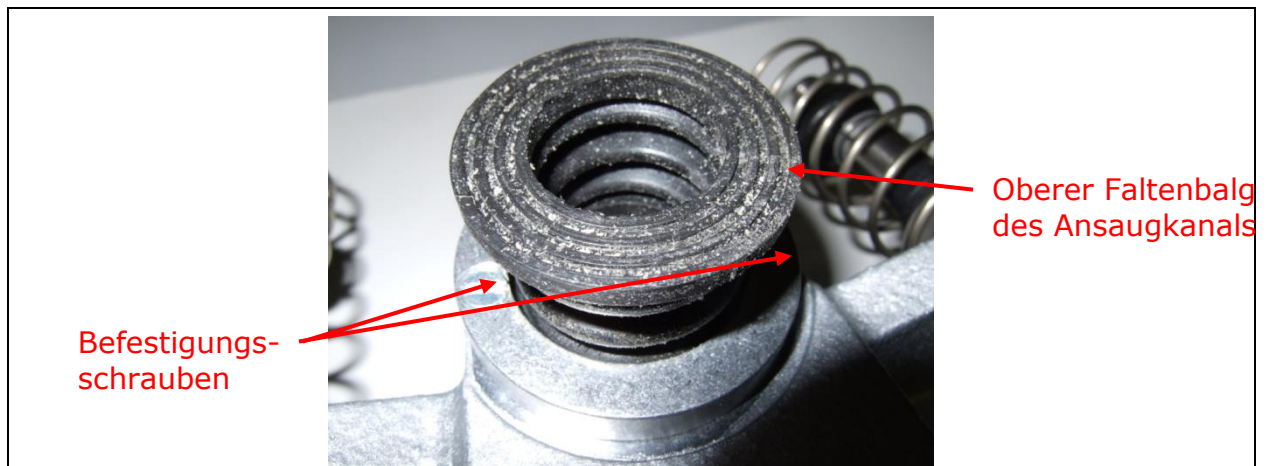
Schritt 4 Beide Faltenbälge ggf. tauschen. Der Faltenbalg ist mit einem mit zwei Schrauben befestigten Ring gesichert.
